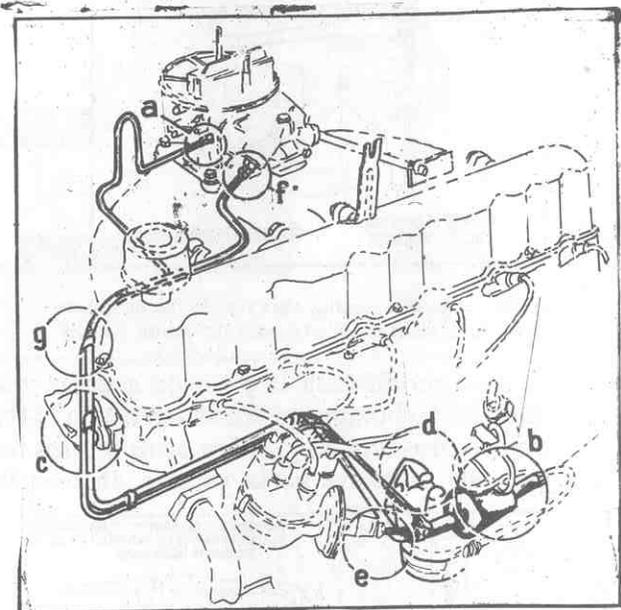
Sistema de combustible del motor 221 SP. Ver también detalles a-g.
